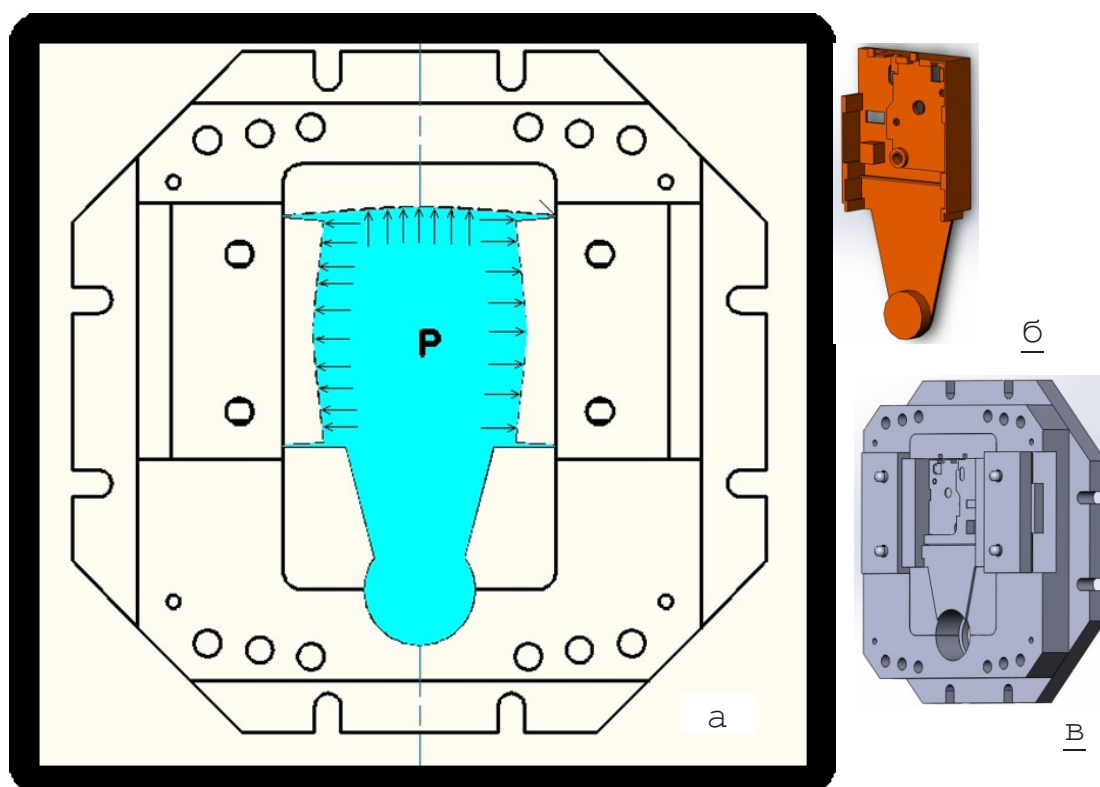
Влияние давления на формообразующие вставки пресс-формы. Где а-вид на подвижную полу-форму; б-отливка; в-подвижная полу-форма; Р-давление металла; 1-возможный прогиб формообразующих вставок и обоймы
